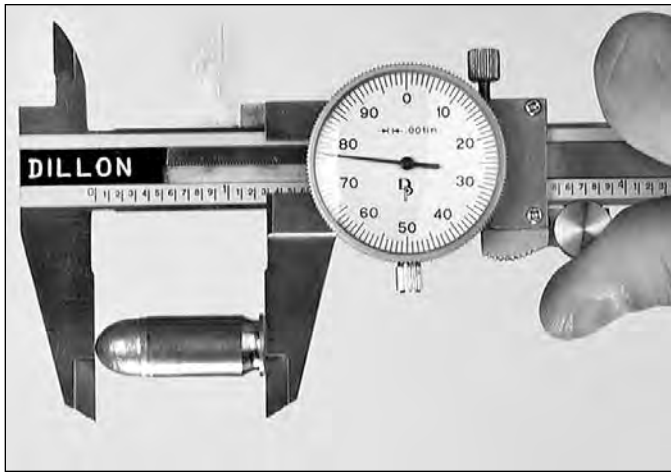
[Figure 29] - Die Gesamtlänge wird mit der Zifferblatt-Schieblehre [dial caliper] gemessen.
